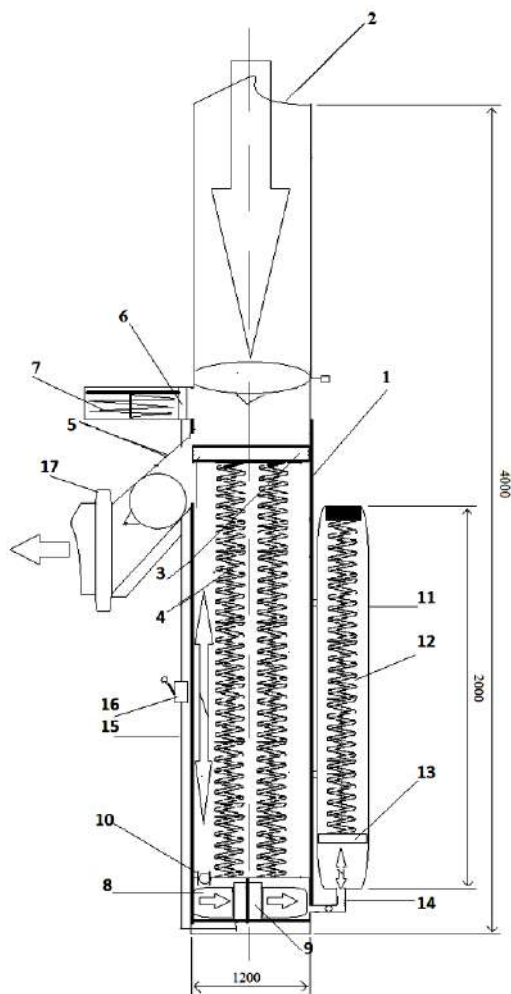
Принципова схема дробильного агрегата с гравітаційно-пневматичним електроприводом (базовий варіант)
